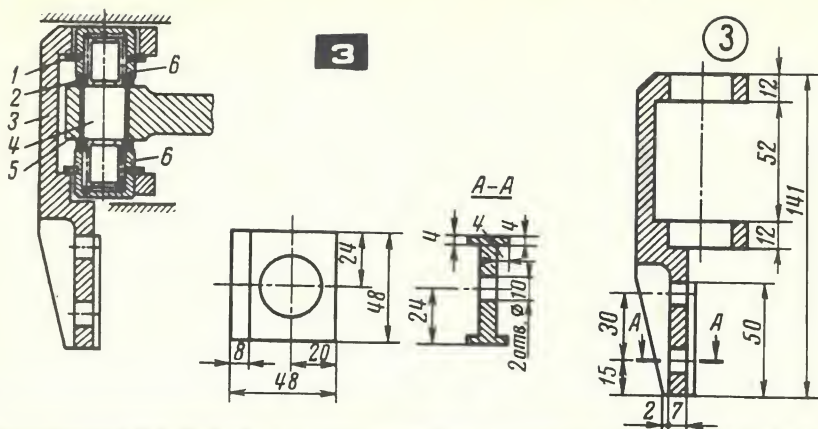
1 — стопорное кольцо; 2 — сальник; 3 — кронштейн; 4 — палец; 5 — рычаг; 6 — подшипник.
